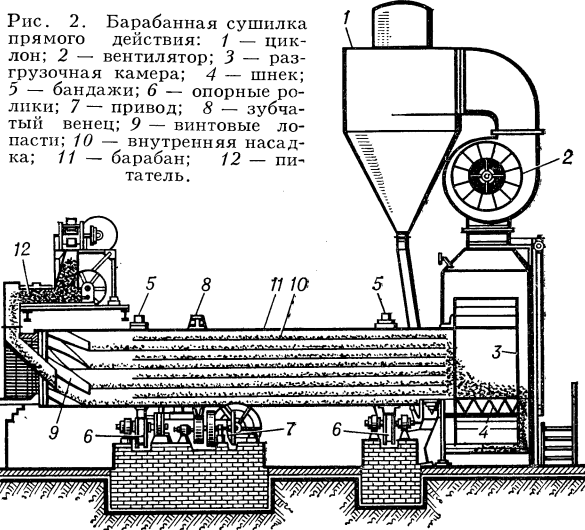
Барабанная сушилка прямого действия: 1 — цилиндр; 2 — вентилятор; 3 — разгрузочная камера; 4 — шнек; 5 — бандажи; 6 — опорные ролики; 7 — привод; 8 — зубчатый венец; 9 — винтовые лопасти; 10 — внутренняя насадка; 11 — барабан; 12 — пилот.
